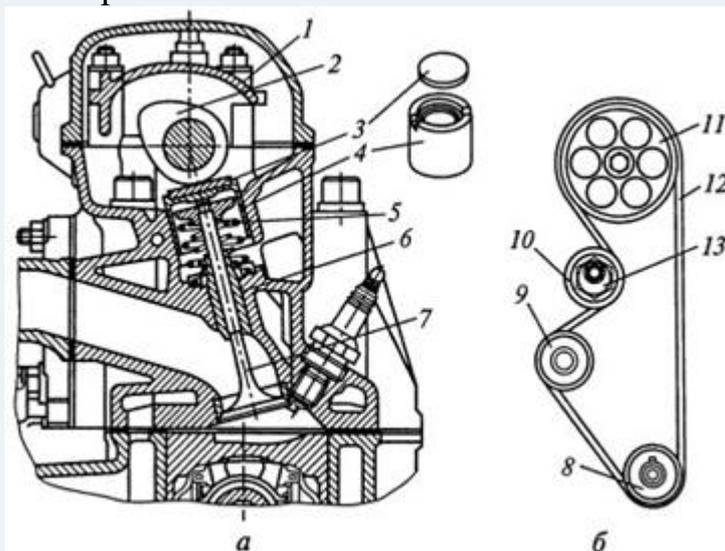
Газораспределительный механизм (а) с верхним расположением распределительного вала и его привод (б): 1 – корпус; 2 – распределительный вал; 3 – шайба; 4 – толкатель; 5 – пружина; 6 – втулка; 7 – клапан; 8, 9, 11 – шкивы; 10 – ролик; 12 – ремень; 13 – ось
